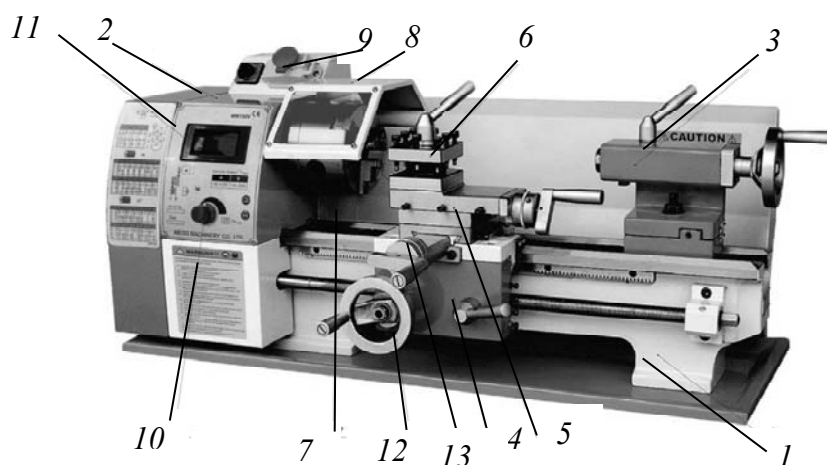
Общий вид токарного настольного станка Universal WM180V
